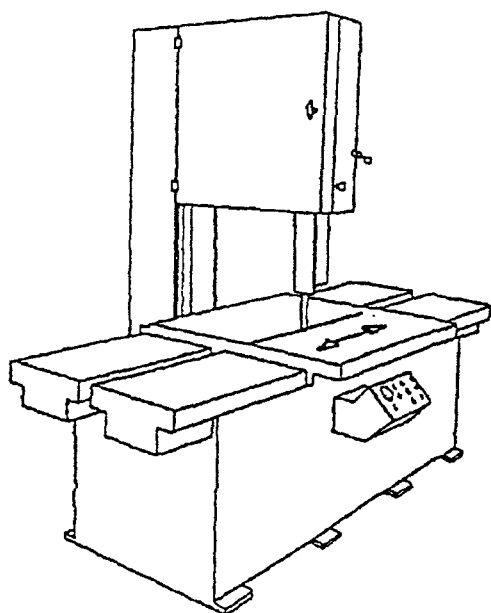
а — Вертикальний стрічковопиляльний верстат з траверсою та подаванням стола
